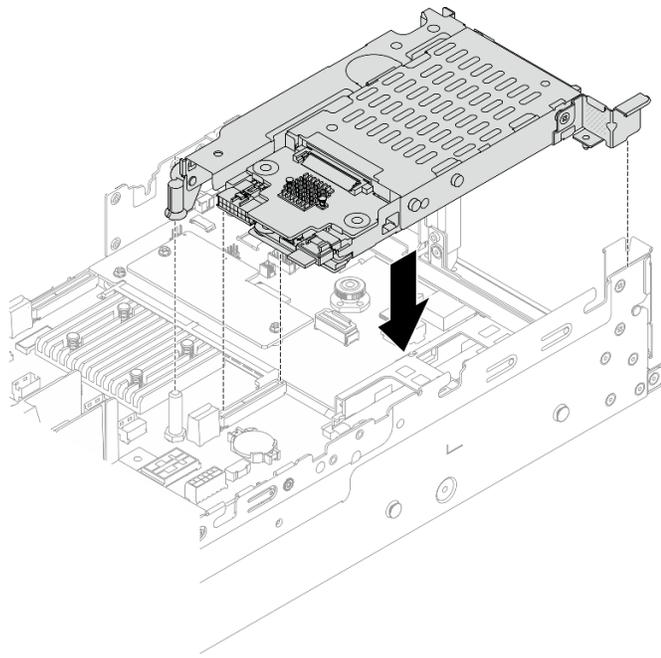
Installation d'un boîtier de carte mezzanine SSD 7 mm
